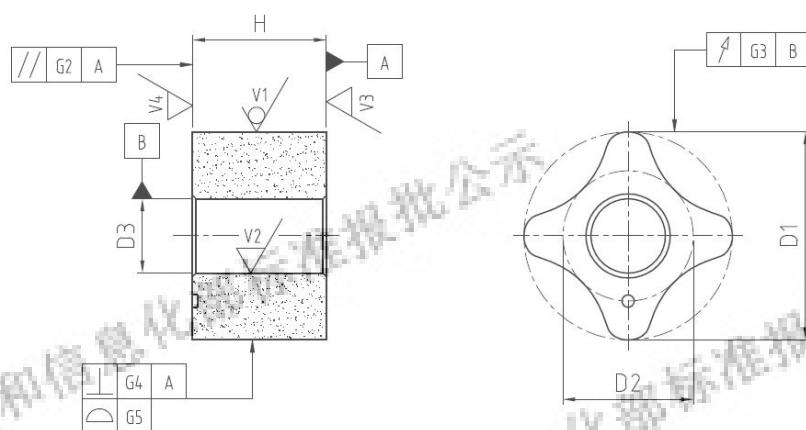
圆形孔定位式内转子尺寸、几何公差及表面粗糙度标注示意图
